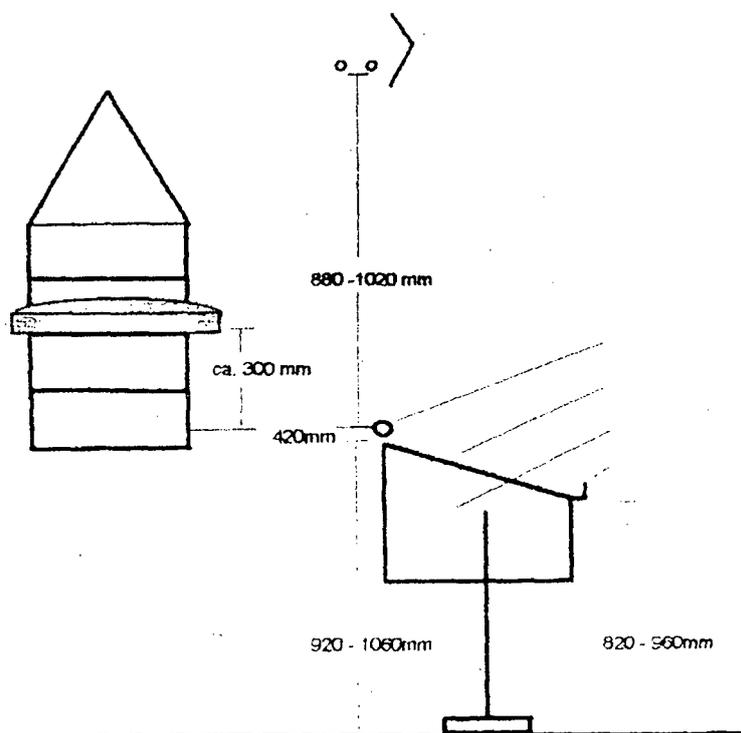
Dimensões gerais da bancada de inspeção a frio.
